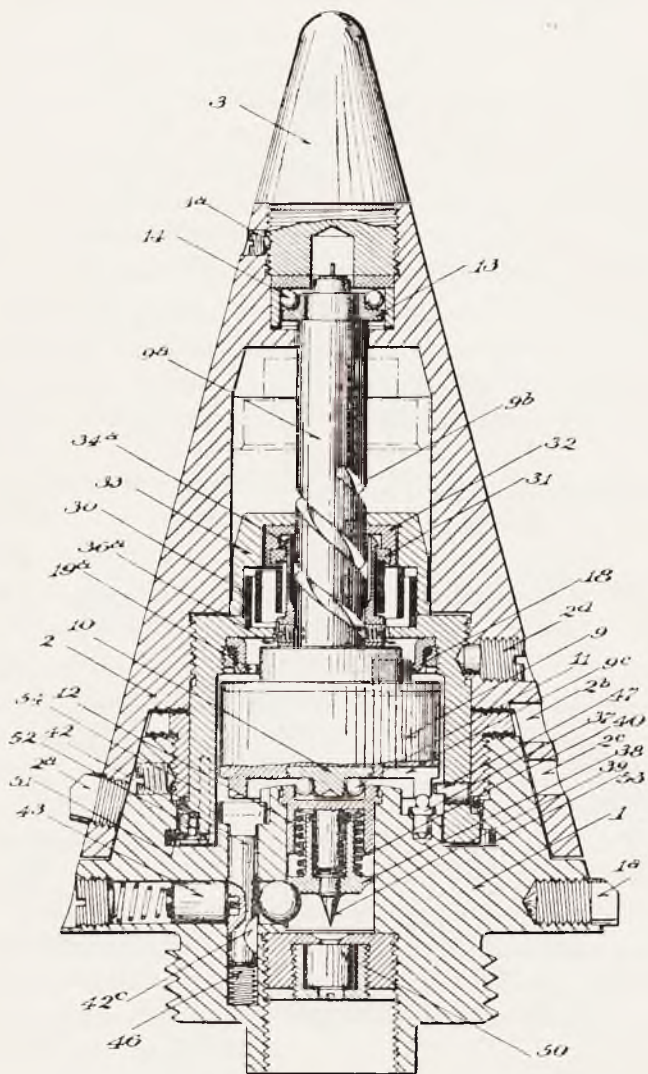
przedstawia zapalnik w takim stanie, jak jest przechowywany w magazynach.
